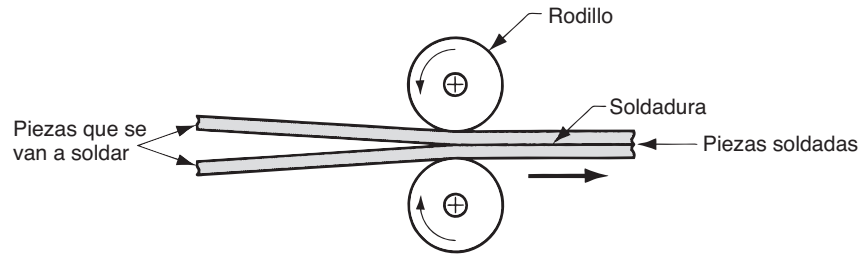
Soldadura con rodillos (ROW).
